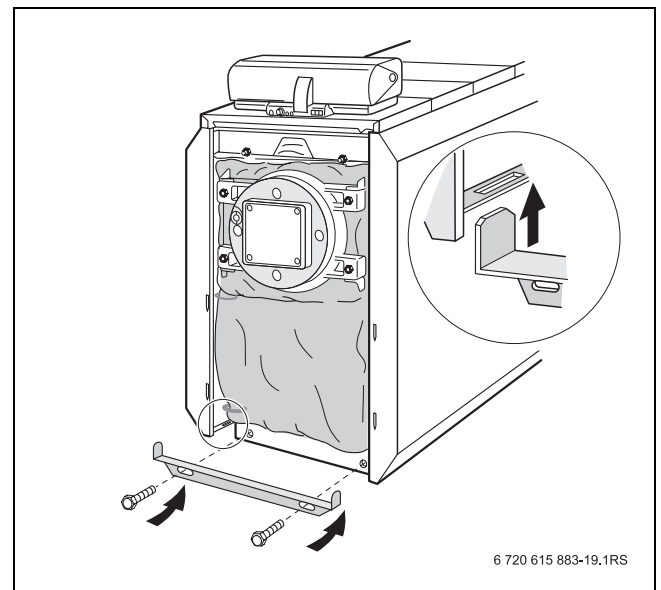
Položení dílů krytu kotle - principiální zobrazení
